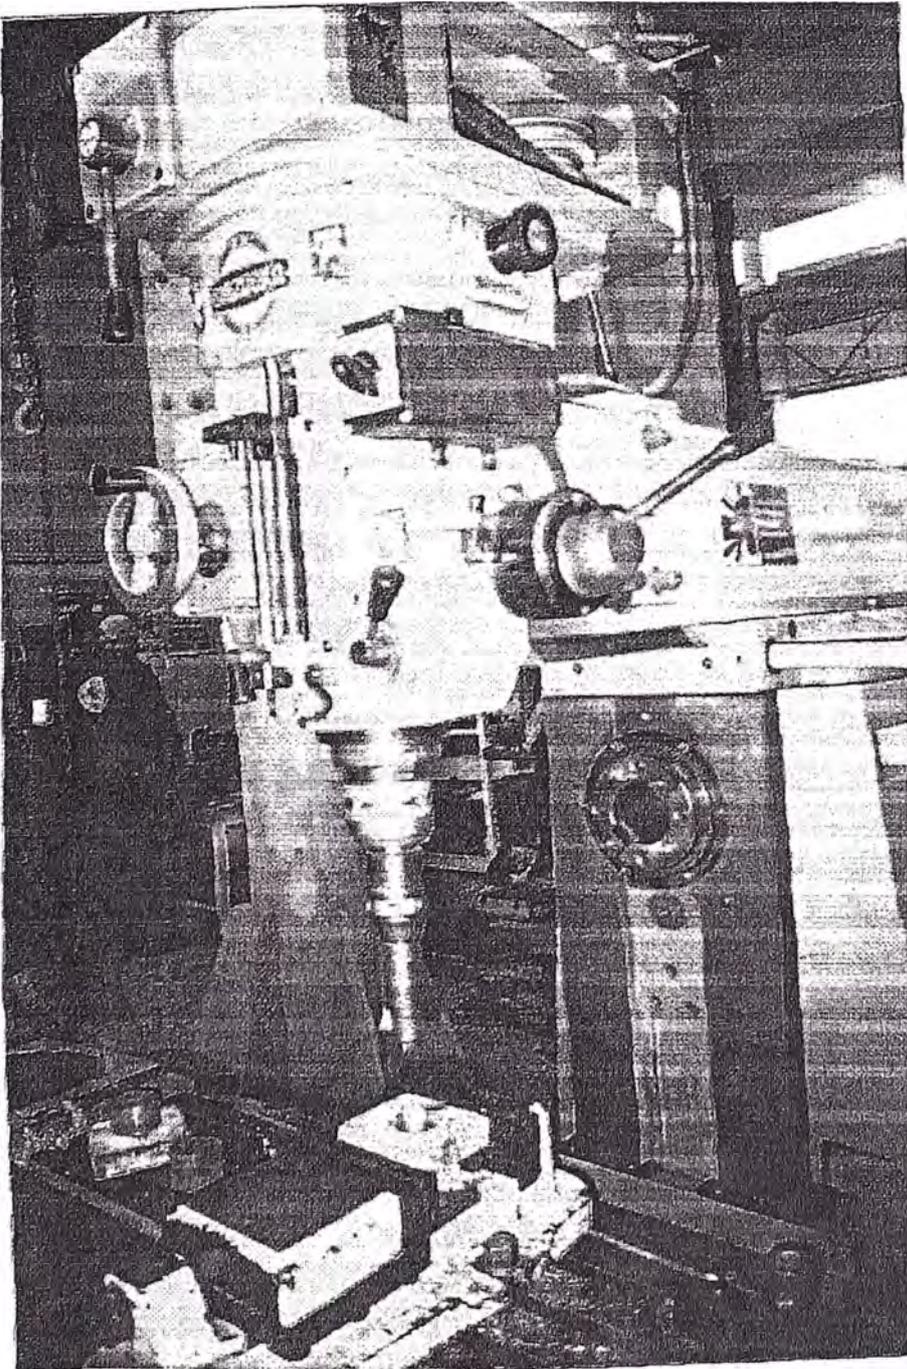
Fresadora Universal Marca Shizuoka
